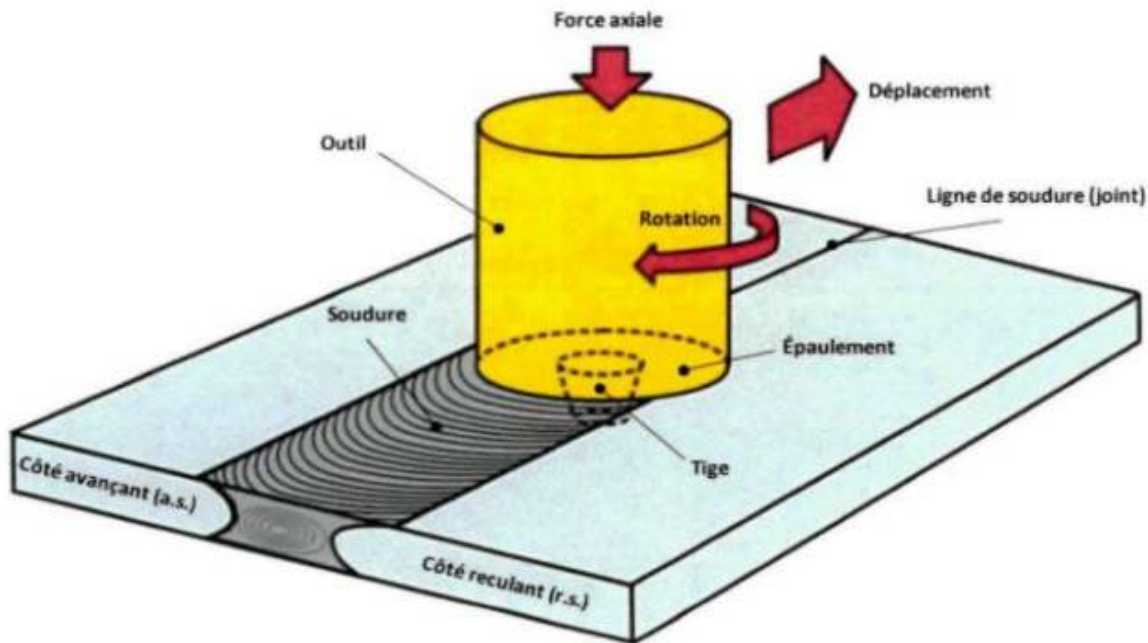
Représentation schématique des plaques et de l’outil de soudage
